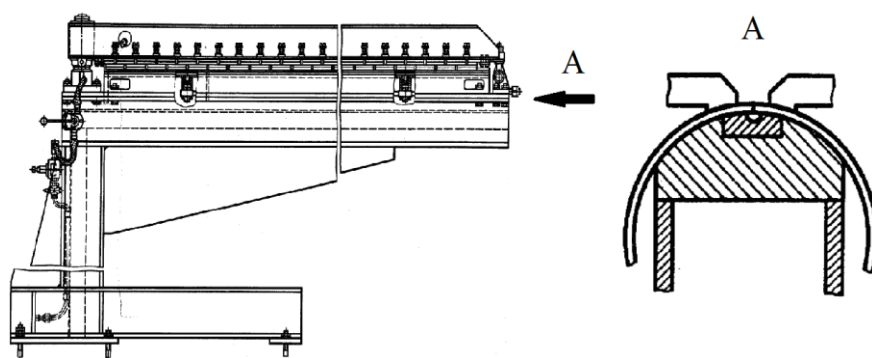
Стенд для сварки продольных швов [72]
